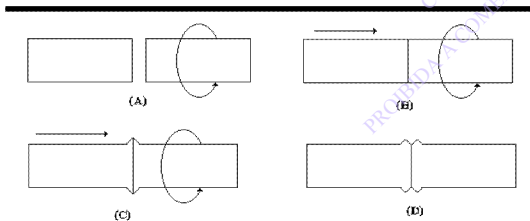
Etapas Características na Soldagem por Fricção.
